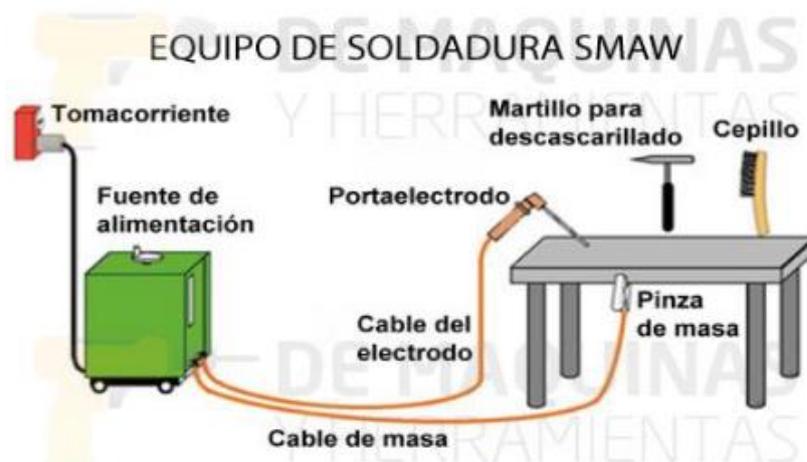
Equipos de soldadura SMAW. Fuente: [19]
